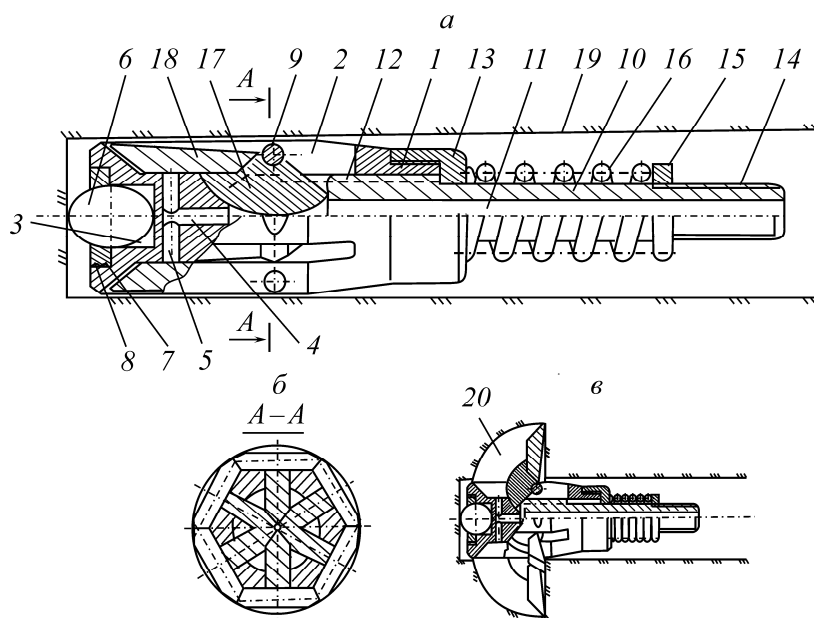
Устройство для образования инициирующей щели поперек скважины: а — продольный разрез в исходном состоянии; б — разрез А-А; в — то же устройство с выдвинутыми резами, продольный разрез; 1 — корпус; 2 — полукруглые канавки; 3 — углубление; 4 — осевой канал; 5 — сквозные радиальные каналы; 6 — шаровая пята; 7 — шайба; 8 — резьба; 9 — ось; 10 — толкатель; 11 — осевое сквозное отверстие; 12 — шлиц; 13 — накидная гайка; 14 — резьба; 15 — гайка; 16 — пружина; 17 — тыльные части резов; 18 — резы; 19 — скважина; 20 — инициирующая щель
